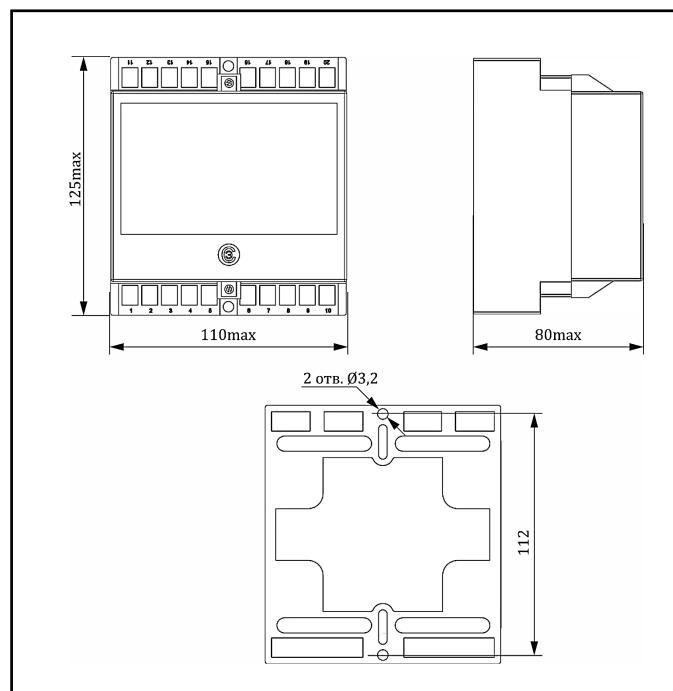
Габаритные и установочные размеры корпуса Е20
